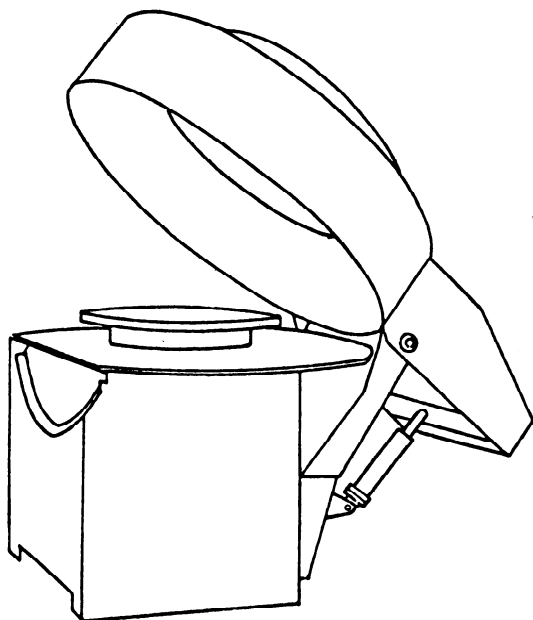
Enceinte type pour rotors sur machine verticale utilisée pour équilibrage en production
